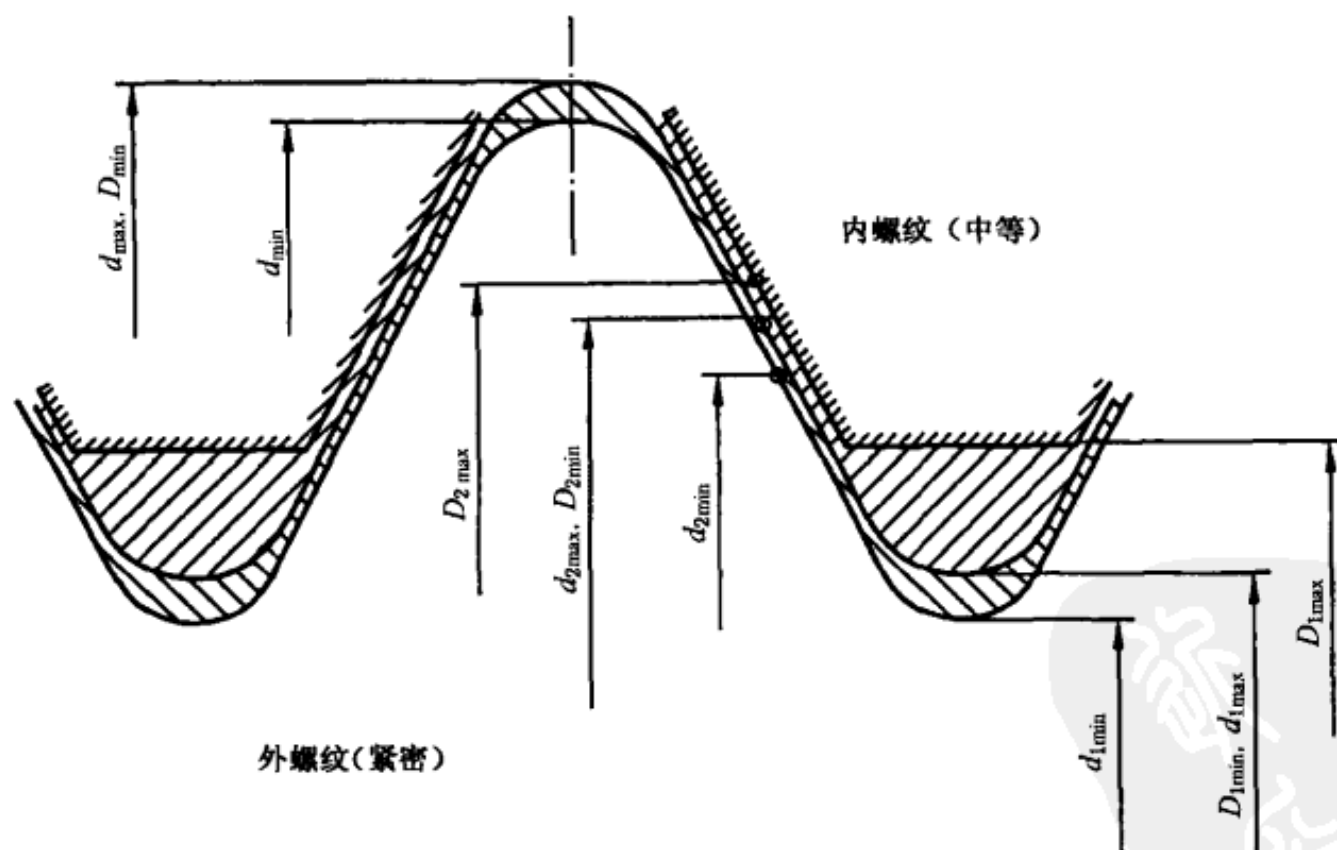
惠氏中等内螺纹与紧密外螺纹配合的公差带位置
